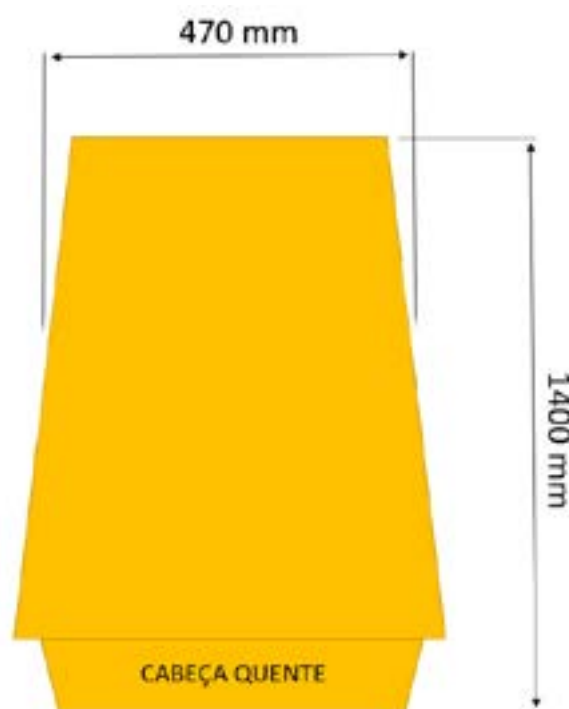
Geometria esquemática em duas dimensões e principais dimensões do lingote 1,95t.
